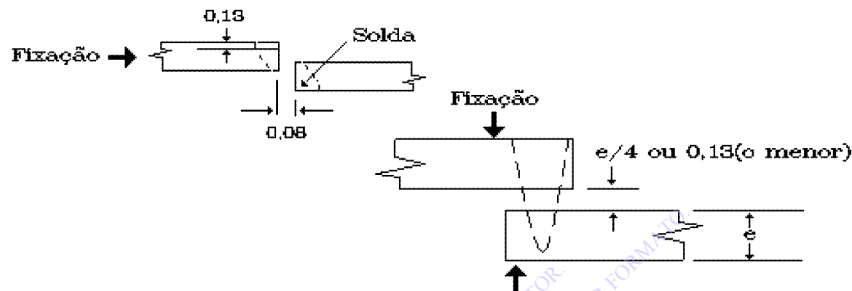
Tolerâncias Dimensionais Típicas (em mm) para Juntas Soldadas por LASER.
